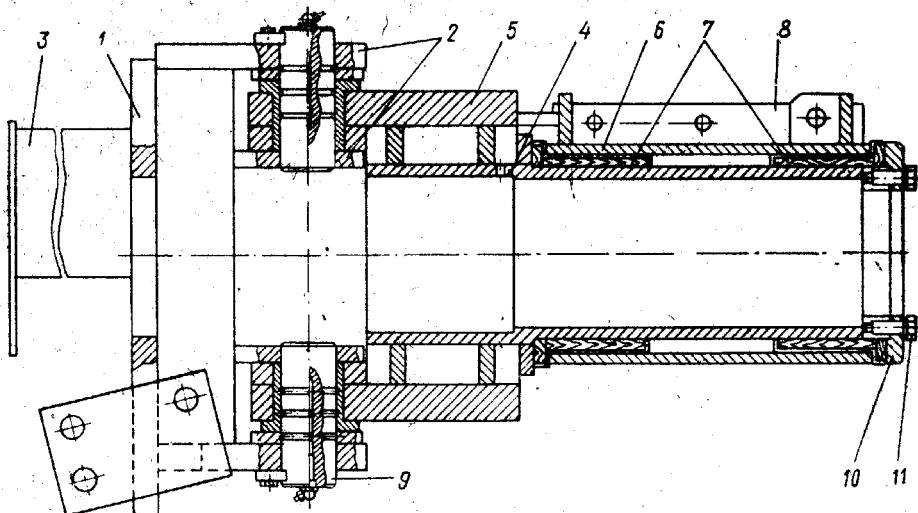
Центральный универсальный шарнир активного полуприцепа в сборе:
